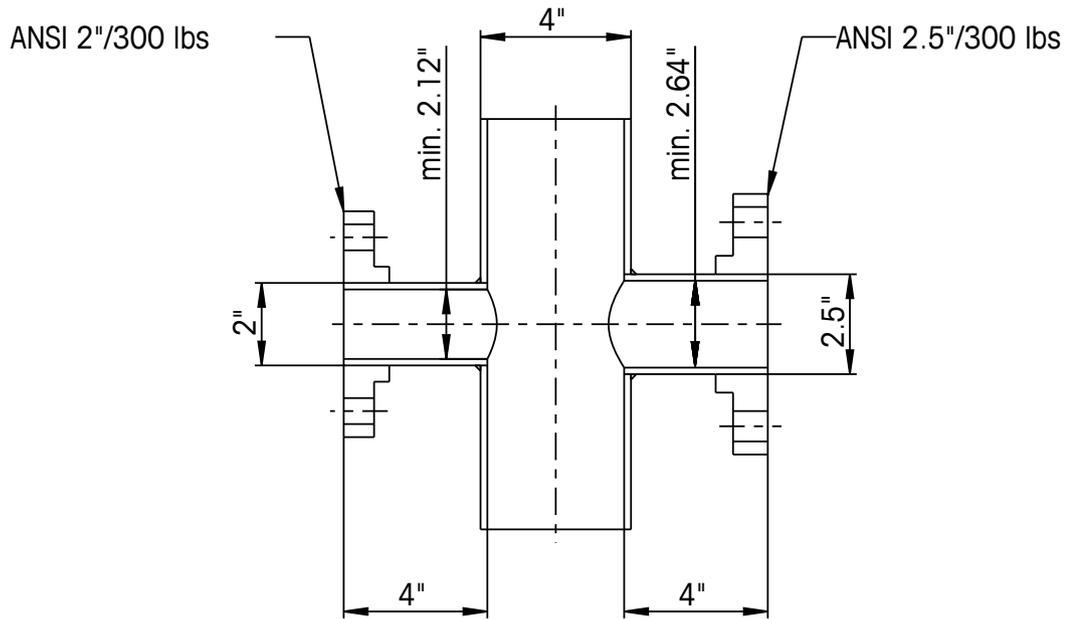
Dimensiones recomendadas para bridas soldadas de sensores con purga estándar (SP), sensores sin purga (NP) y sensores con retroceso (B)
